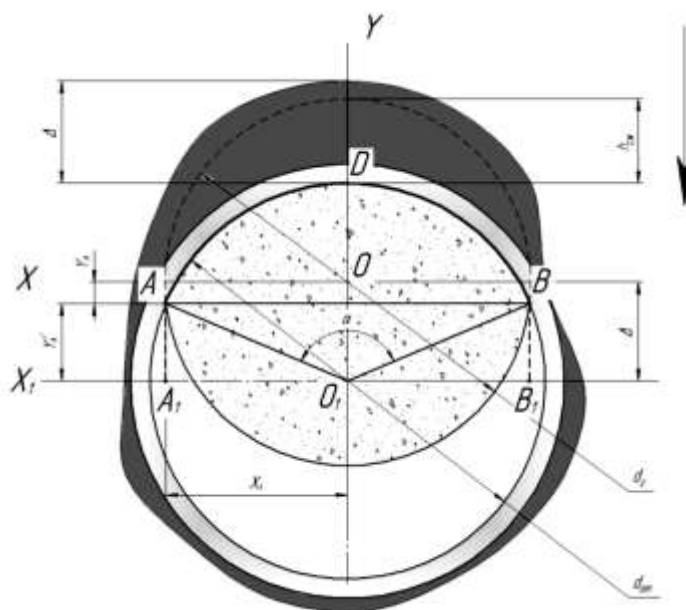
Схема для определения рабочей длины режущей кромки
